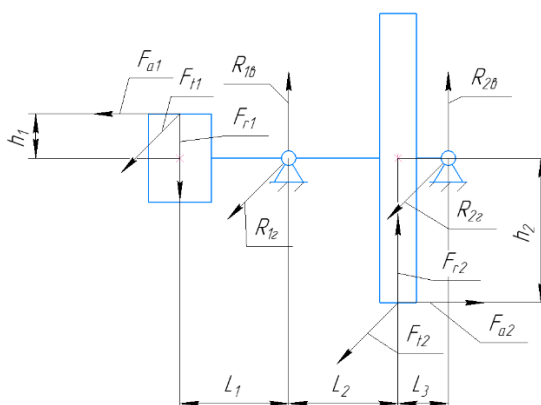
Расчетная схема для подбора подшипников промежуточного вала
